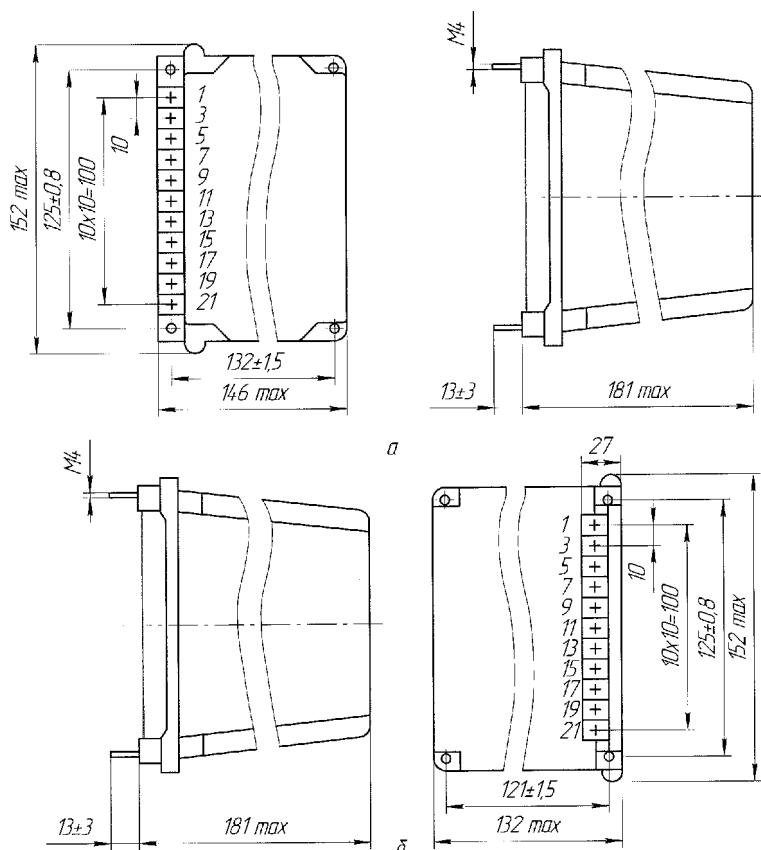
Габаритные, установочные и присоединительные размеры реле PCG 11.
